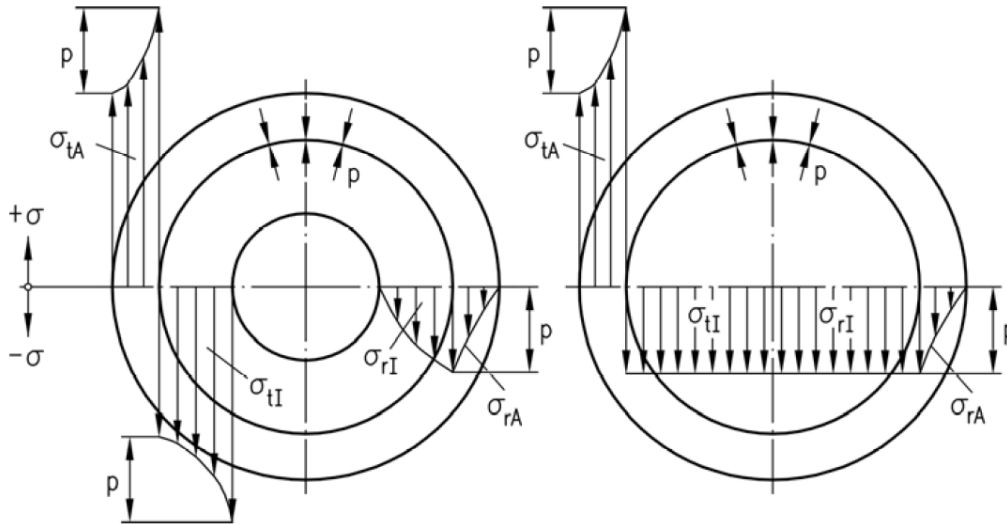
Verlauf der Radial- und Tangentialspannungen im Querschnitt einer elastisch beanspruchten Pressverbindung; Hohlwelle (links) und Vollwelle (rechts) [5]
